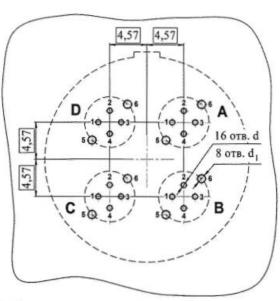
Схема расположения отверстий для установки соединителя СКЦ102-4/21 . . . печатного монтажа
